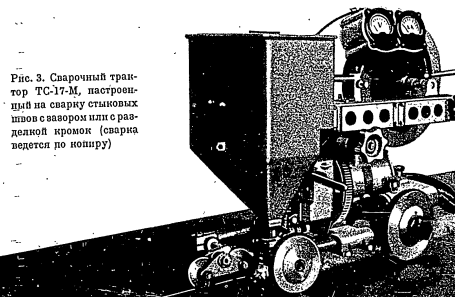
Сварочный трактор TC-17-M, настроенный на сварку стыковых швов с разделкой кромок (сварка ведется по шпильке)
